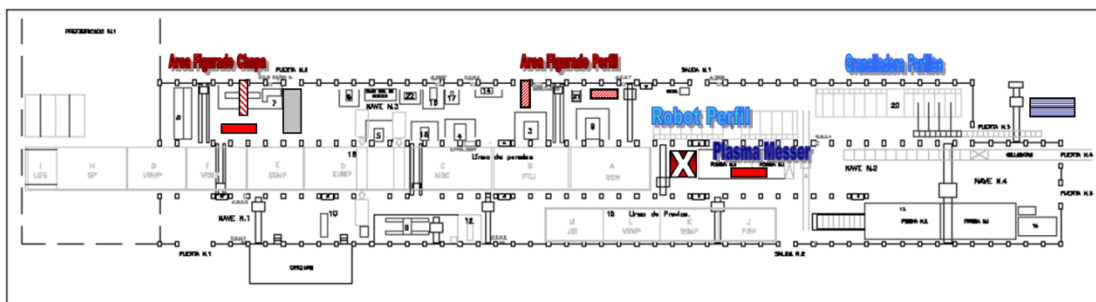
Disposición el planta taller de elaboración (Fuente Academia Lean Navantia)
